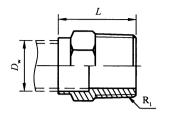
外螺纹转换接头承插式钎焊铜管件
